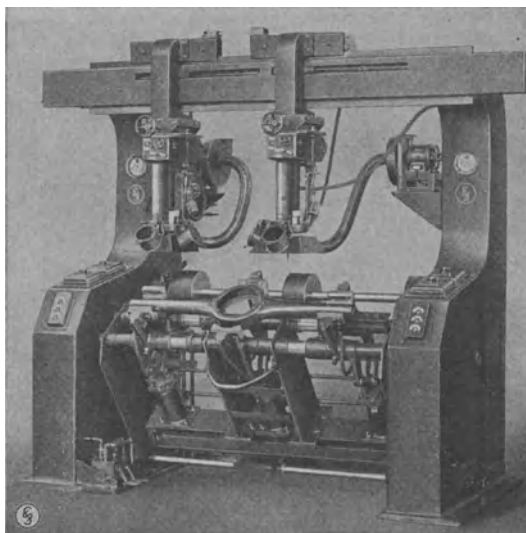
Selbsttätige Schweißmaschine für Hinterachsbrücken.
